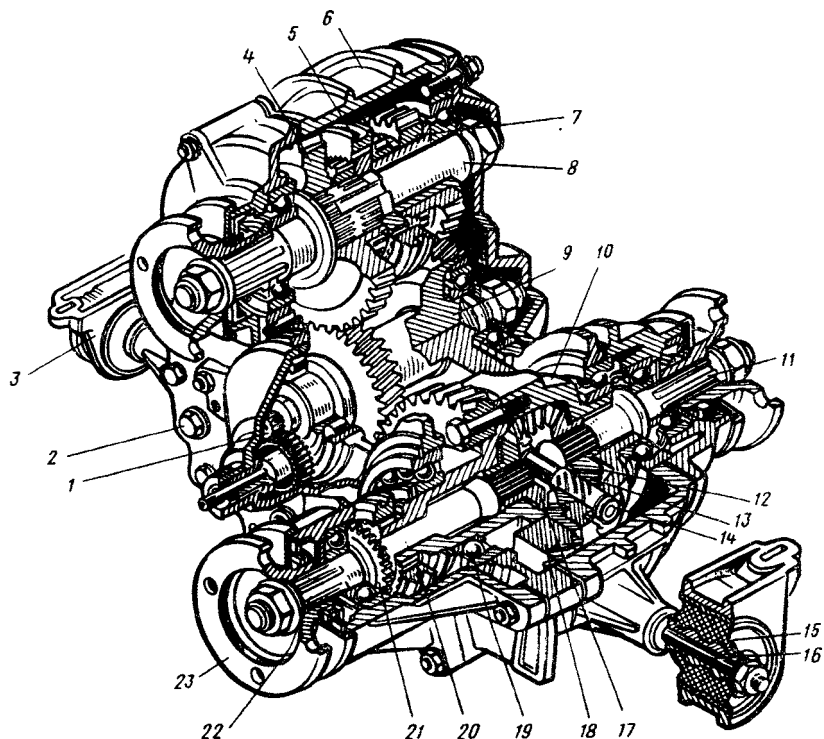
Раздаточная коробка автомобиля ВАЗ-2121:
